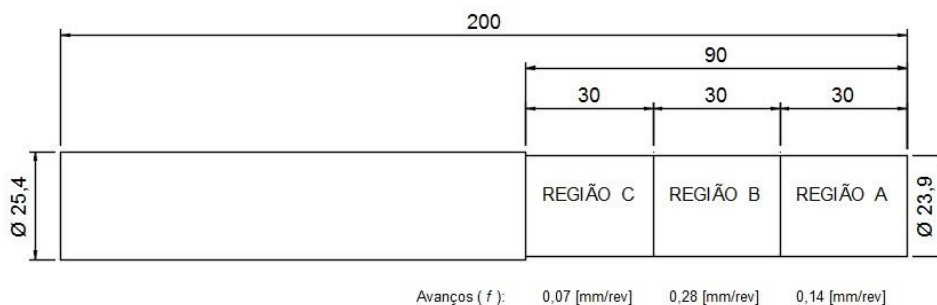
Desenho das regiões definidas para a usinagem do corpo de prova
